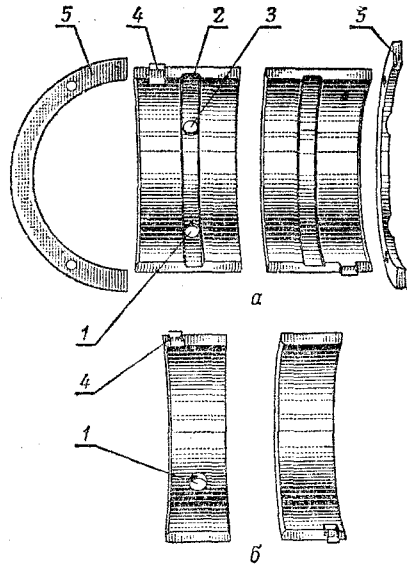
Вкладыши коренных подшипников дизеля СМД-14:
